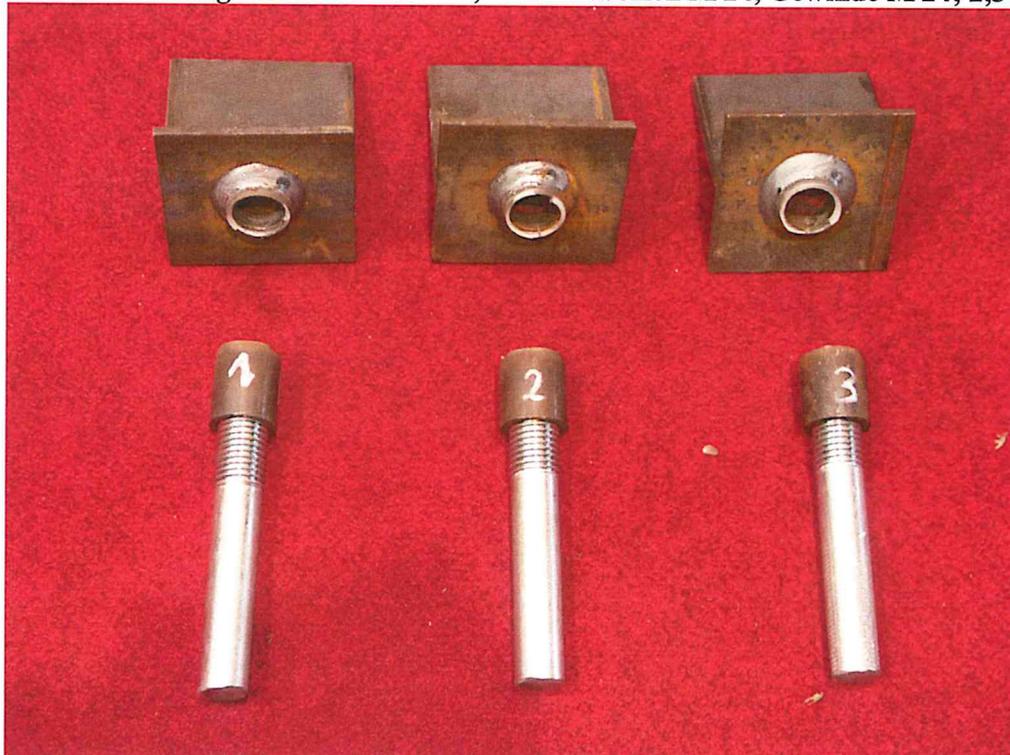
Bruchlagen Flachstahlanker, Gewindebolzen M 30, Gewinde Rd 30; 4 t
